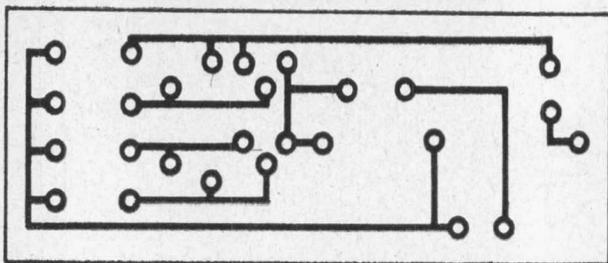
Sugestão para o circuito impresso do injetor. O desenho refere-se à face cobreada da plaqueta.
